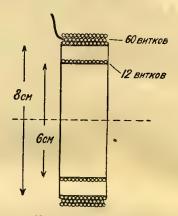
Нейтродинный коденсатор с сотовой обмоткой.
